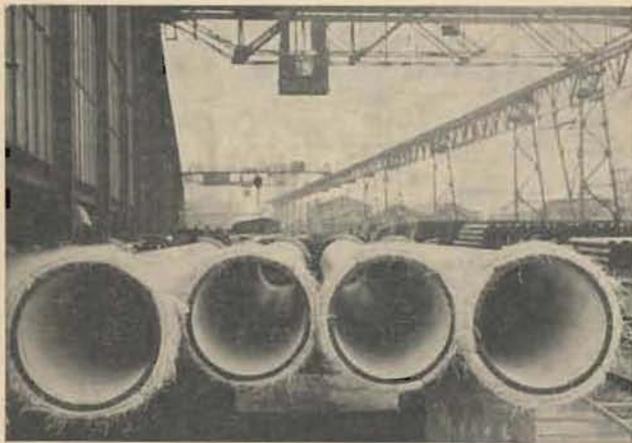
Gußeiserne Druckrohre mit Zementmörtelauskleidung
